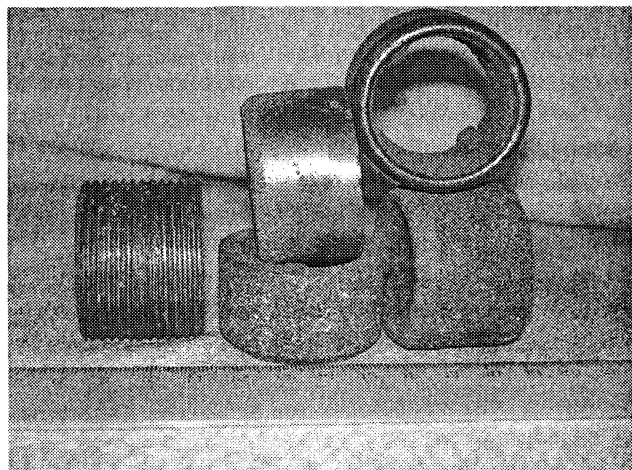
Внешний вид отливок «ниппель 1¼» различной длины
